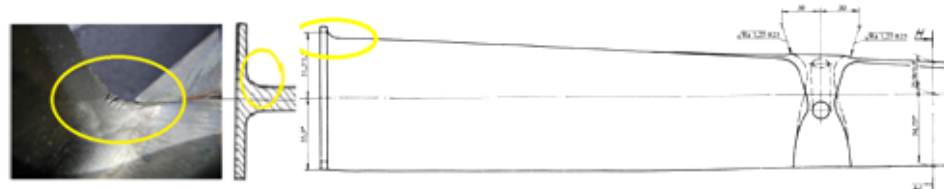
Ділянка лопатки, що не доступна для загартування СВЧ
